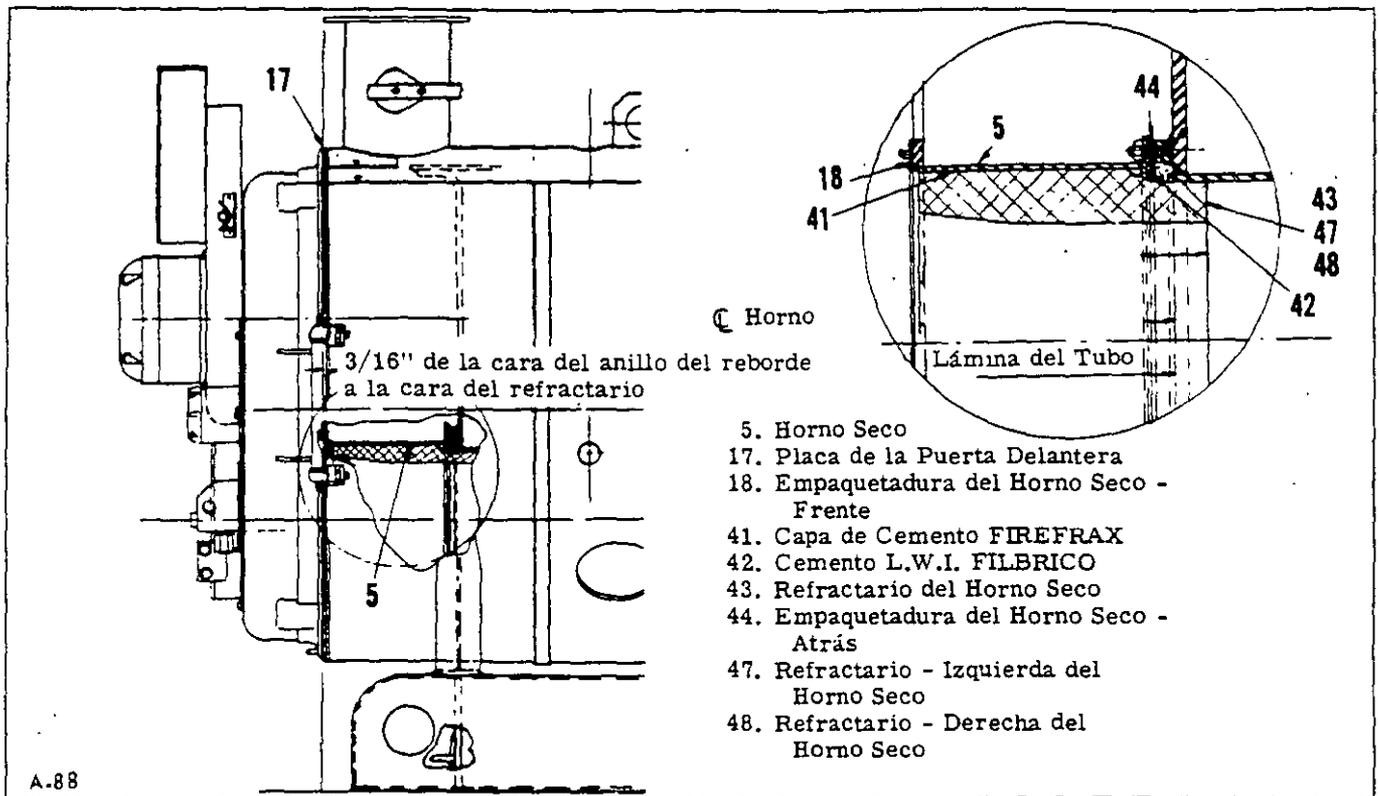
Detalle del Conjunto del Horno Seco
